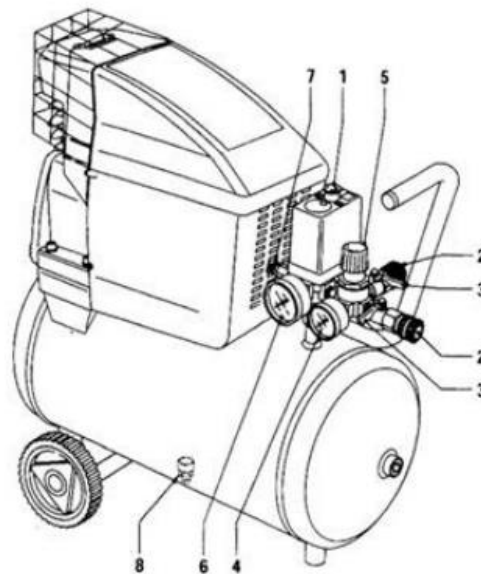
Основные элементы поршневого воздушного компрессора:
